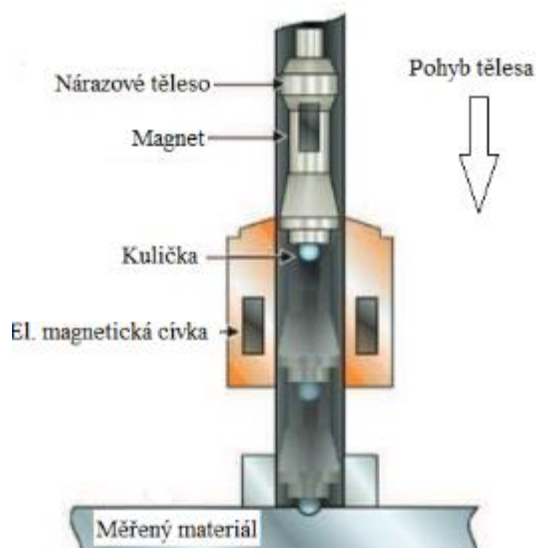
Princip fungování Poldi kladívka pro měření tvrdosti HB [10]
